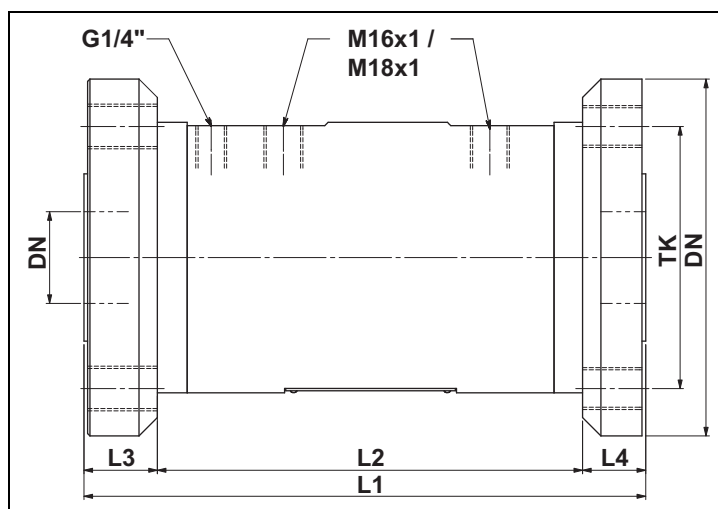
Maßzeichnung OMP mit DIN-Flansch
